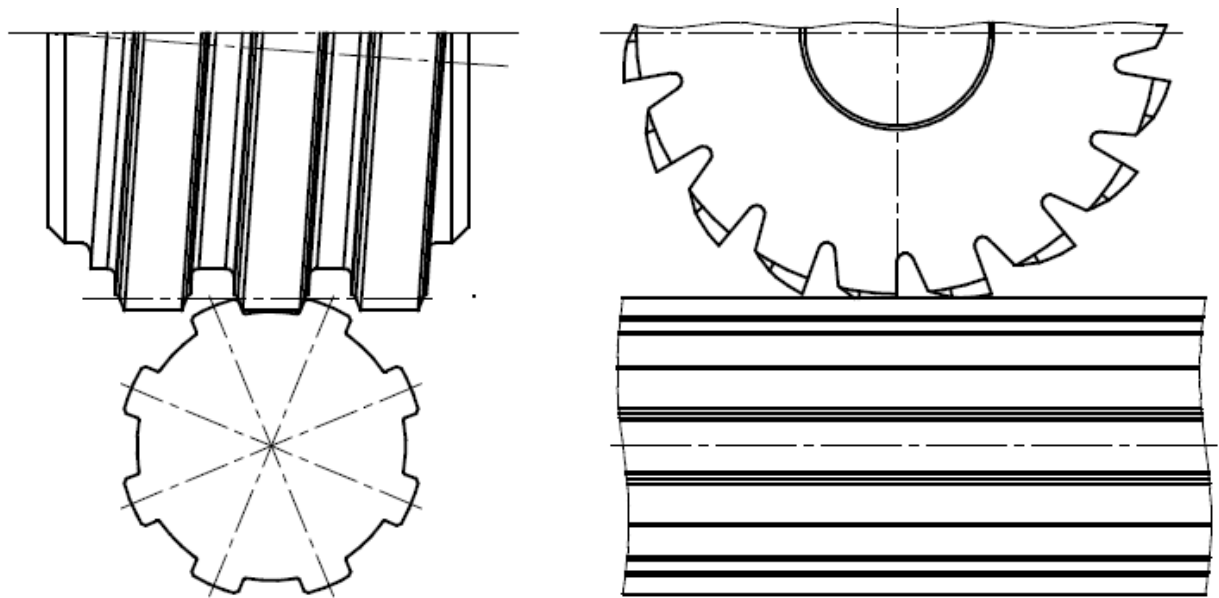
Обробка шліців черв'ячною фрезою
